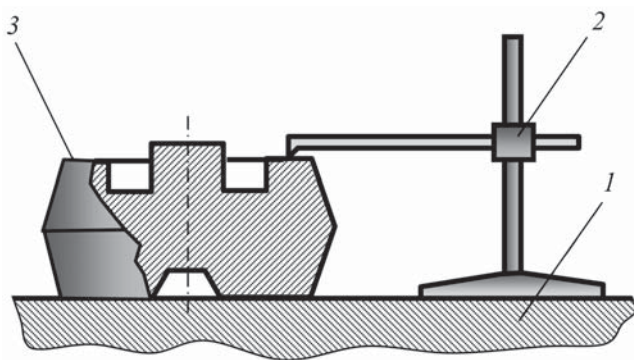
Схема измерения высоты поковки с помощью универсального штангенрейсмаса:
